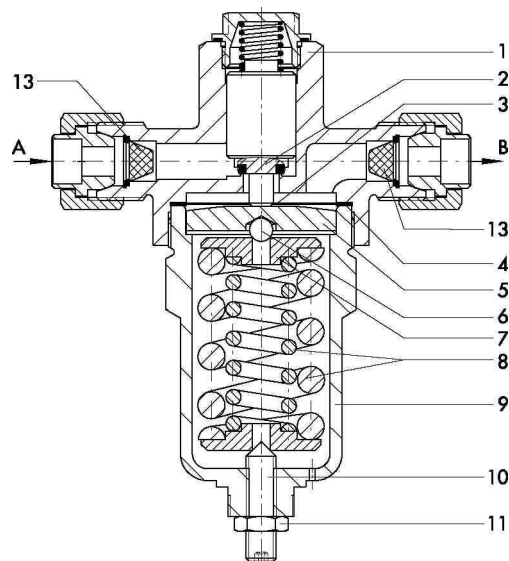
Регулятор восстановления давления или редуктор давления Тип 2357-1/6
